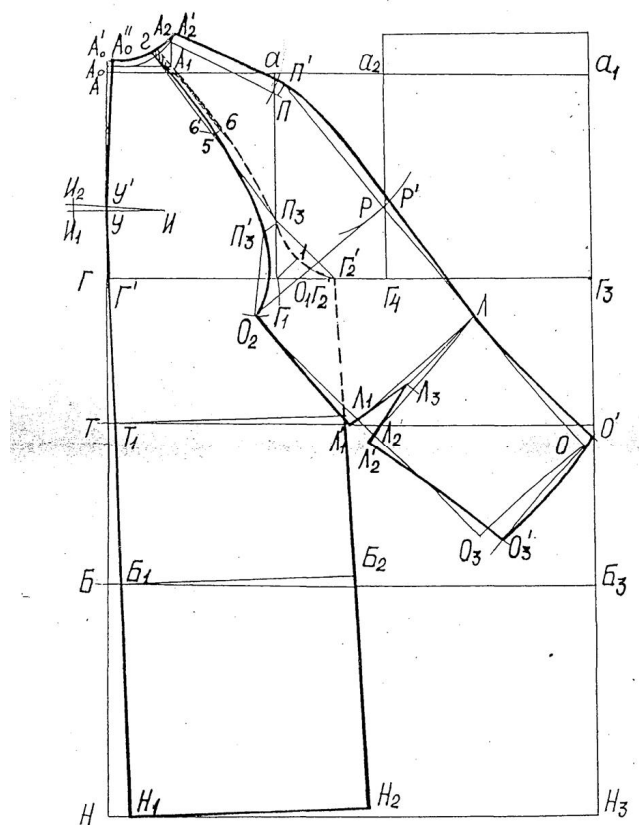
Чертеж конструкции задней части рукава покроя реглан
